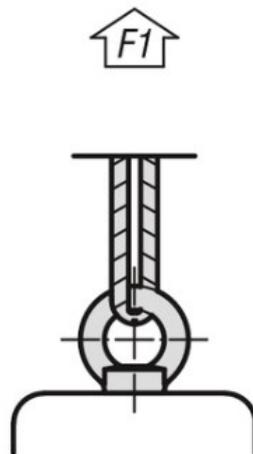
Zulässige Belastungsrichtung beim Verheben mit Ringschrauben
